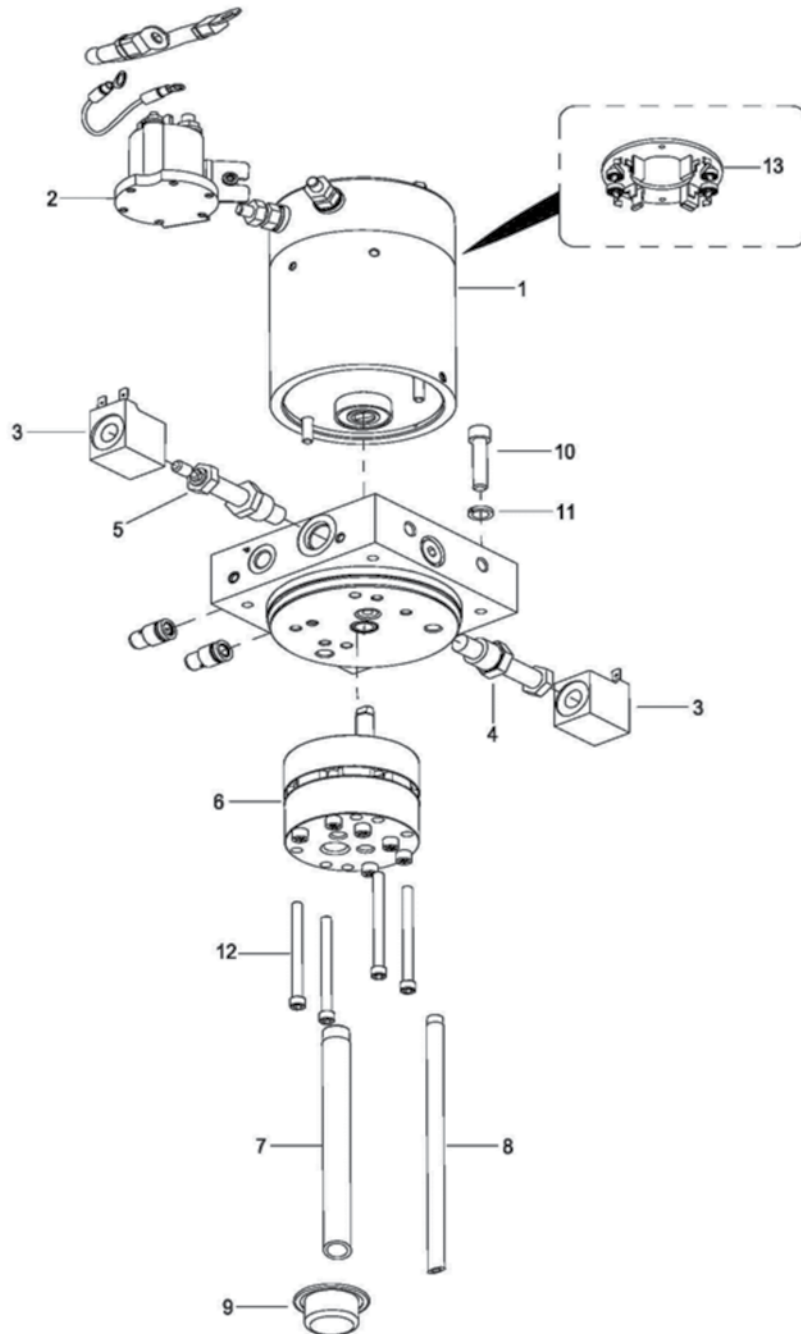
ASSEMBLAGE POMPE ET MOTEUR
